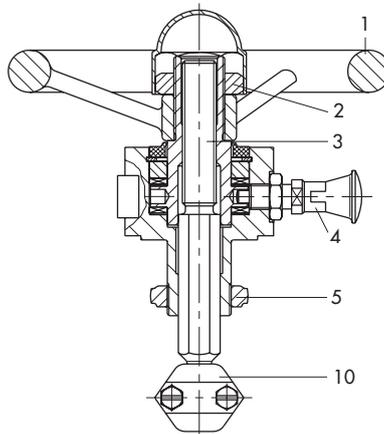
Ручной привод Тип 3273, чертёж в разрезе
